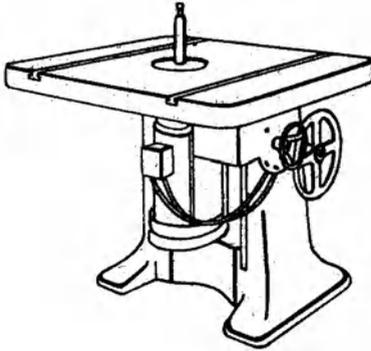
Tischfräsmaschine mit direkt gekuppeltem Elektromotor.
